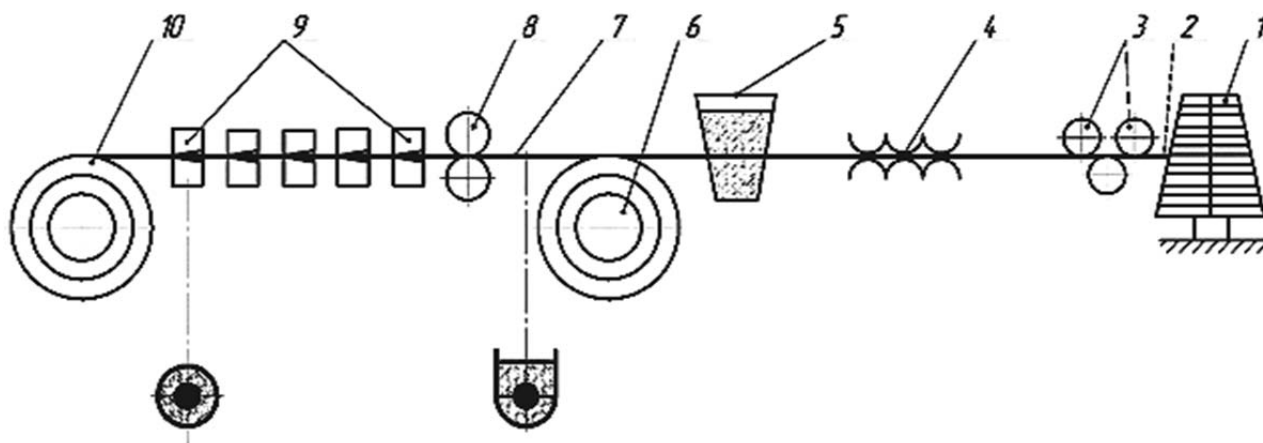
Загальний вид технологічної схеми виготовлення порошкового дроту
